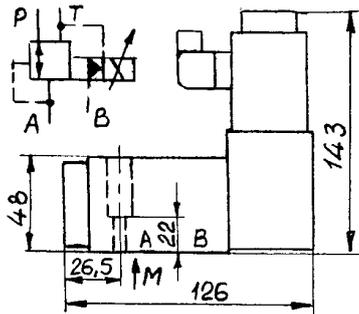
Клапаны VMY*06 Hydraulik-Ring
